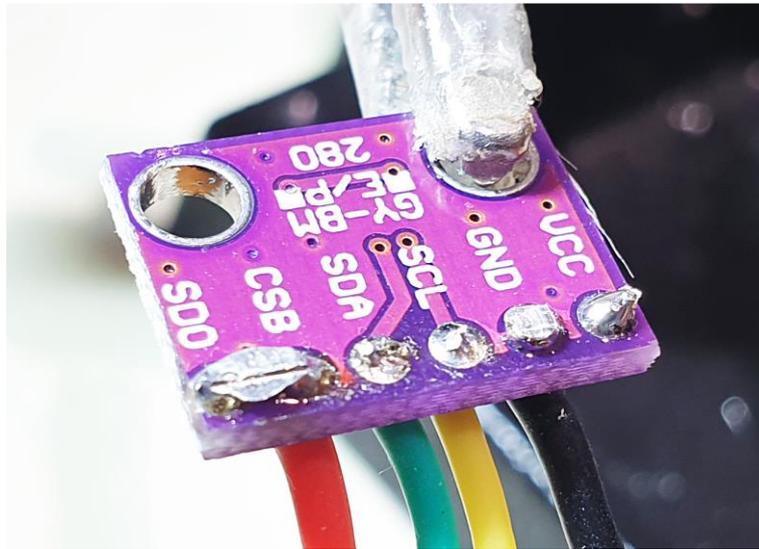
Le résultat de la soudure de l'ensemble des fils
